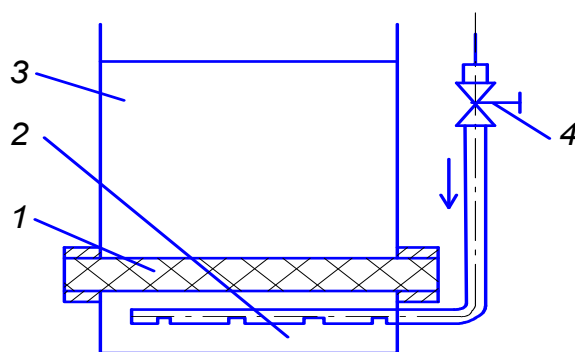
Схема аппарата для нанесения порошков полимеров вихревым способом:
